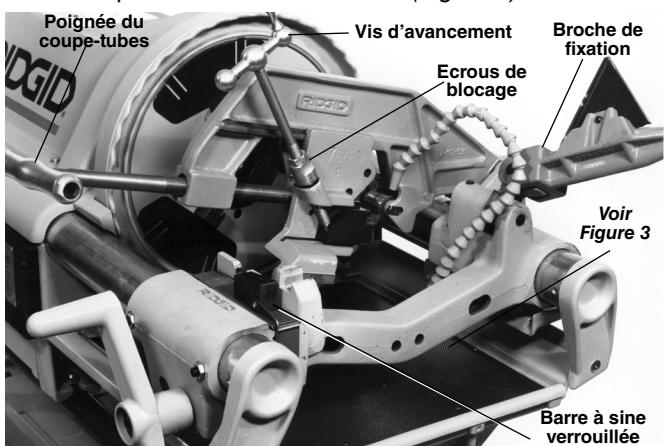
Coupe-tubes à couteau n° 766 installé (avec tête de filetage)
